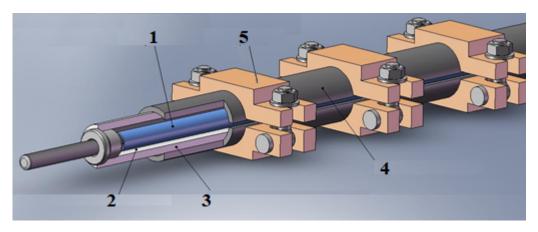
Общий вид устройства с пресс-формой (1 – металлический дорн с антиадгезионной оболочкой, 2 – рабочая поверхность пресс-формы, 3 – корпус пресс-формы, 4 – бандаж, 5 – зажимы)
